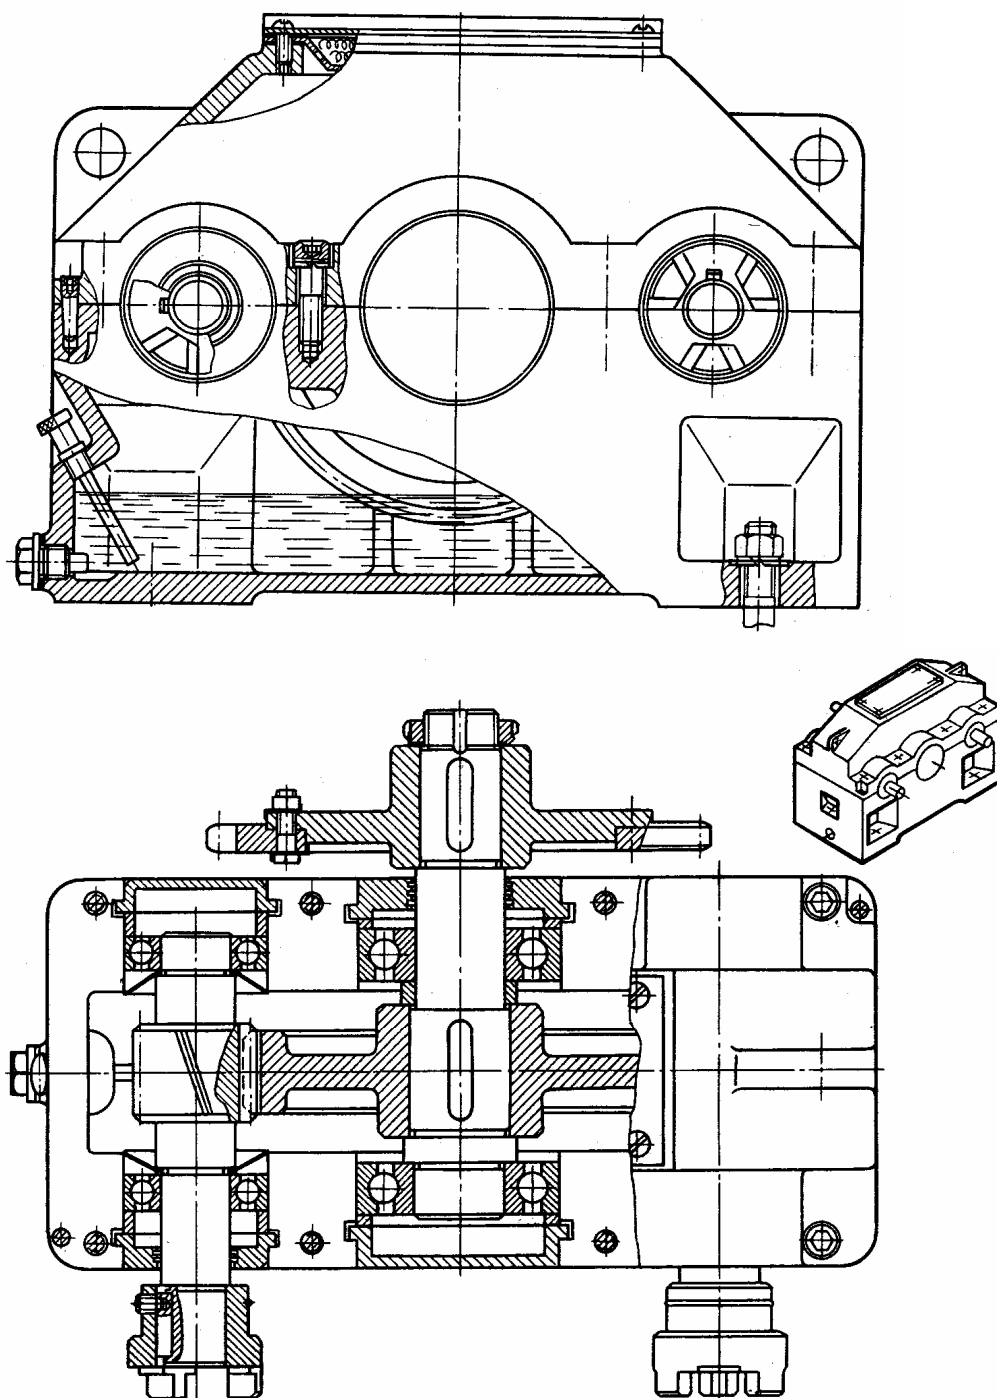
Редуктор (А1) цилиндрический одноступенчатый горизонтальный двухпоточный (с двумя быстроходными валами)
